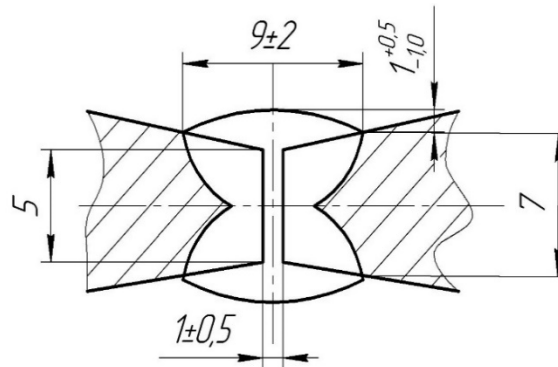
Экспериментальный данные сварного шва
